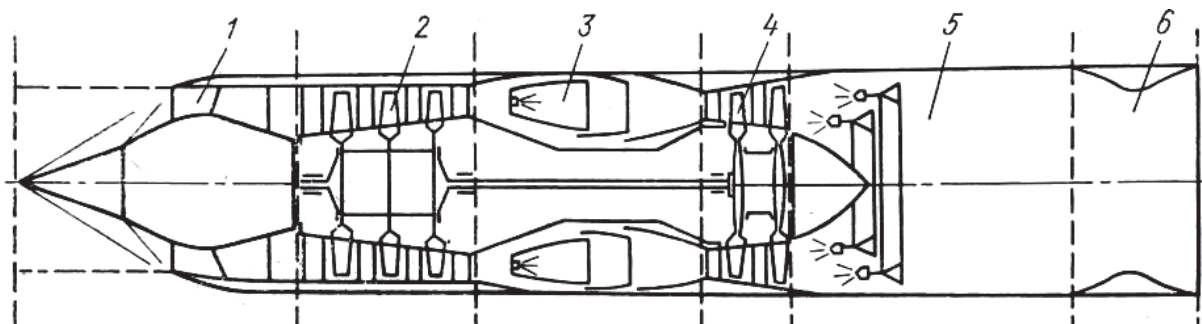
Принципиальная схема турбореактивного двигателя с форсажной камерой сверхзвукового самолета
